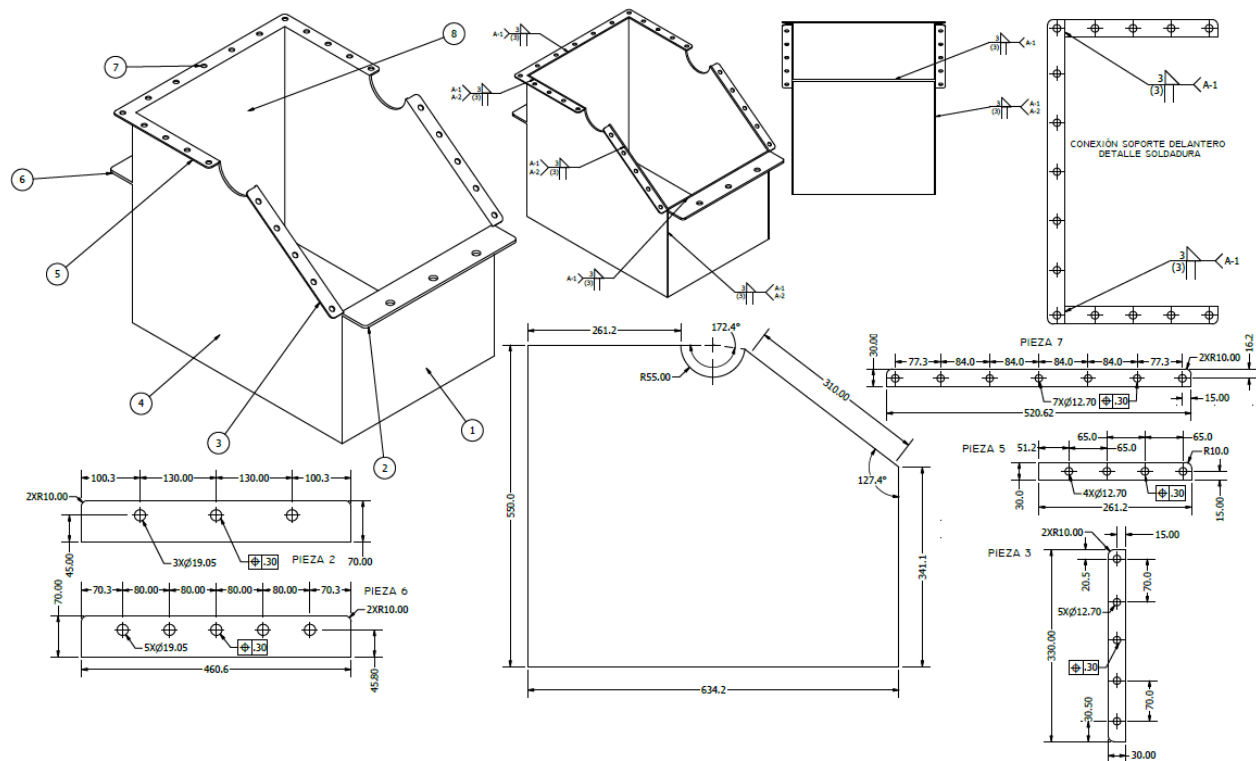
Plano de ensamble soldado: Carcasa inferior. Detalle de componentes, incluyendo brida.
